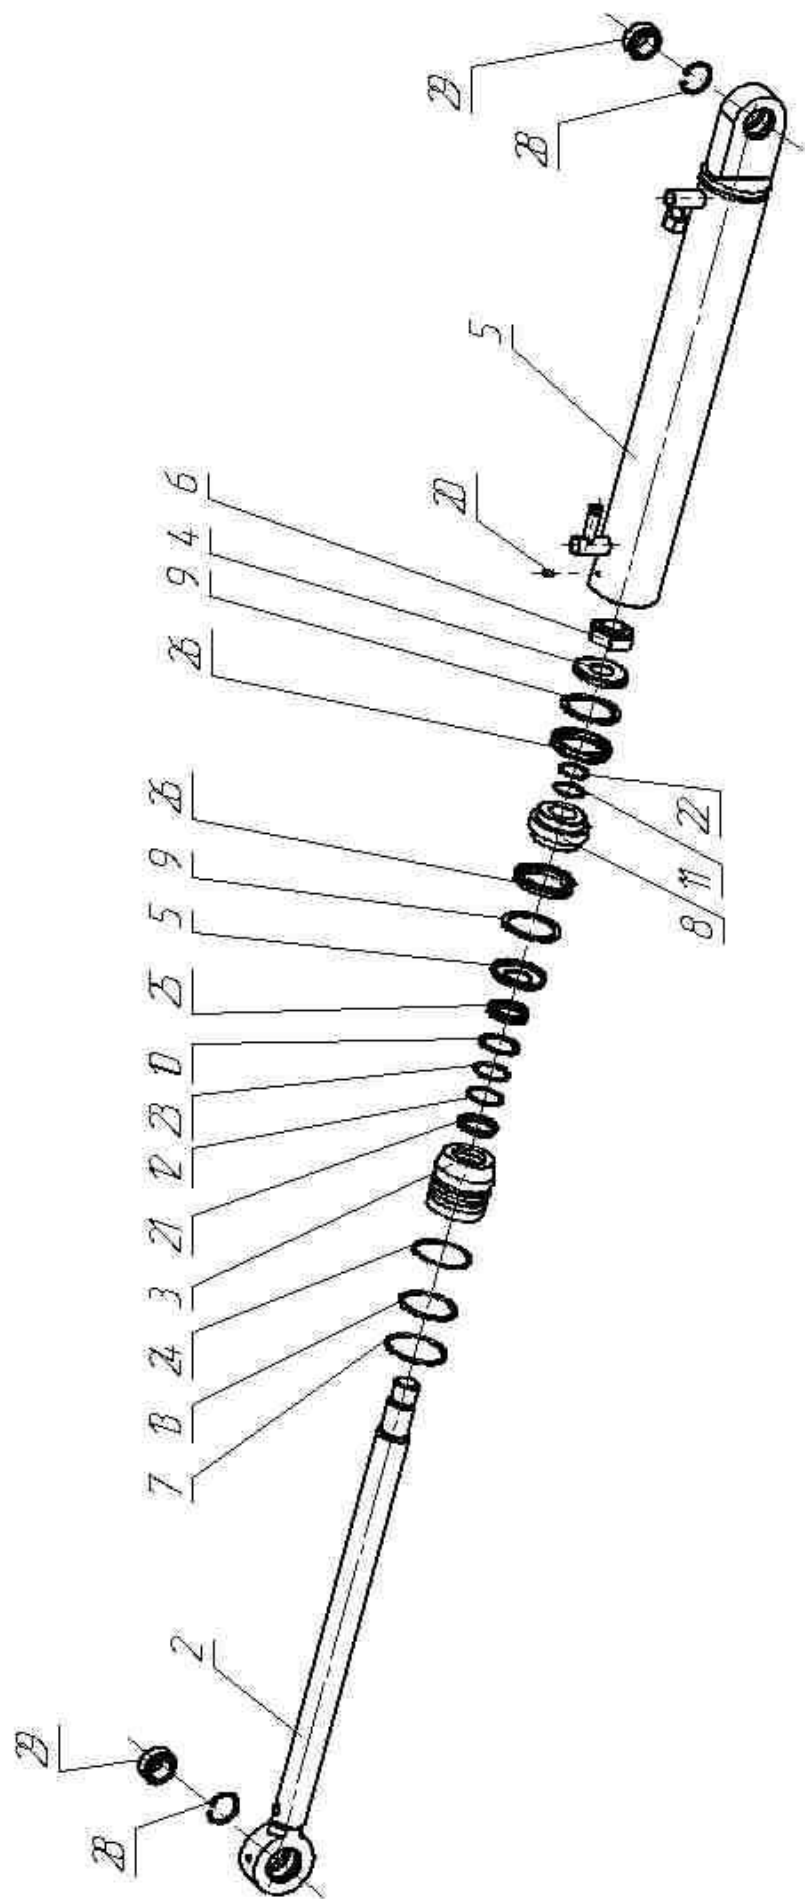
Гидроцилиндр поворота рукоятки КОРС-1100.03.100
